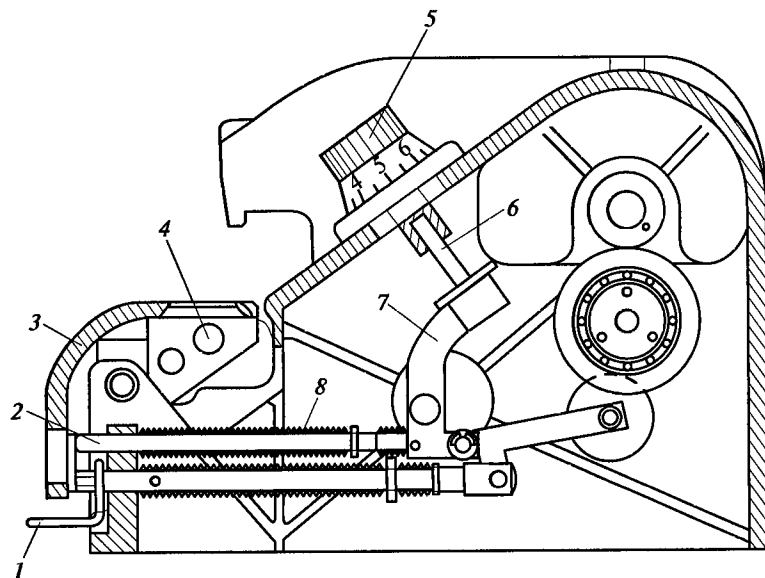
Конструктивная схема узла дополнительного подъема выдавливателя
